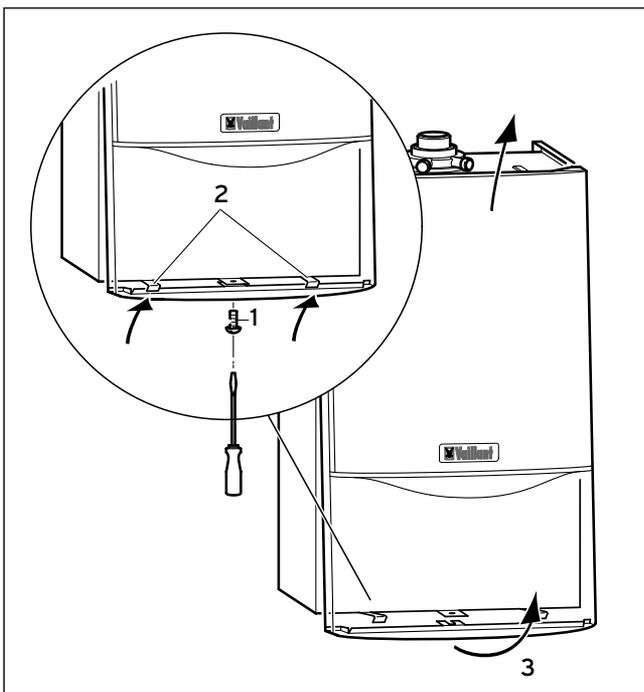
Geräteverkleidung abnehmen/anbringen
